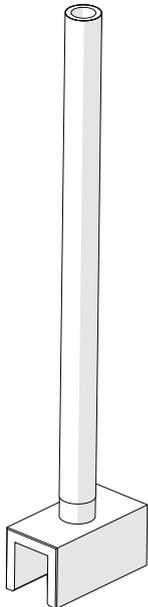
Richtwerkzeug 0812 Verdrillung (Bestell-Nr.: 08-W100-0594)
